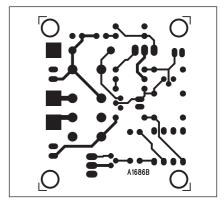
Obrazec desky spojů alarmu (strana TOP)
